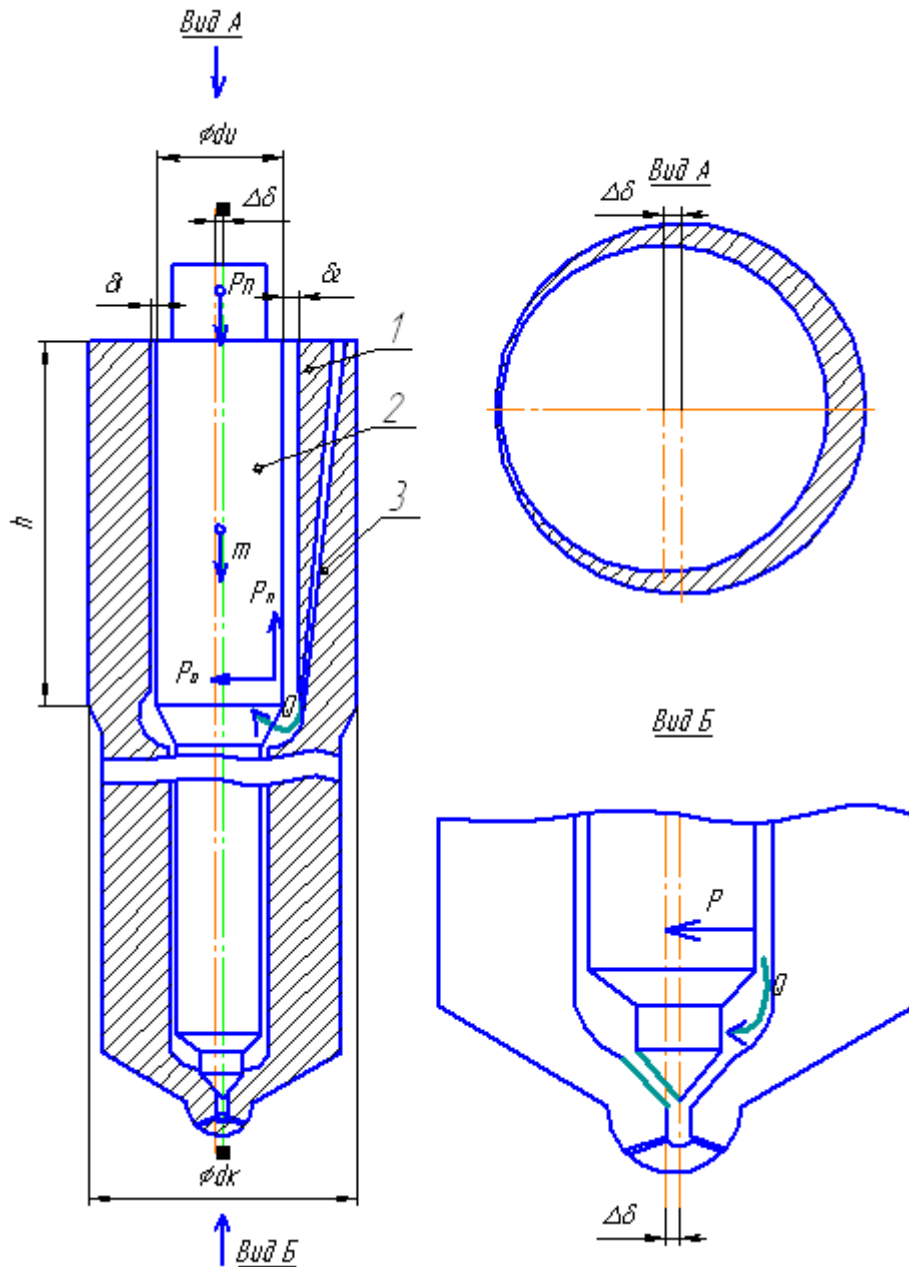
Схема сил, діючих на голку розпилювача: 1 - корпус; 2- голка; 3 - паливоподаючий канал
